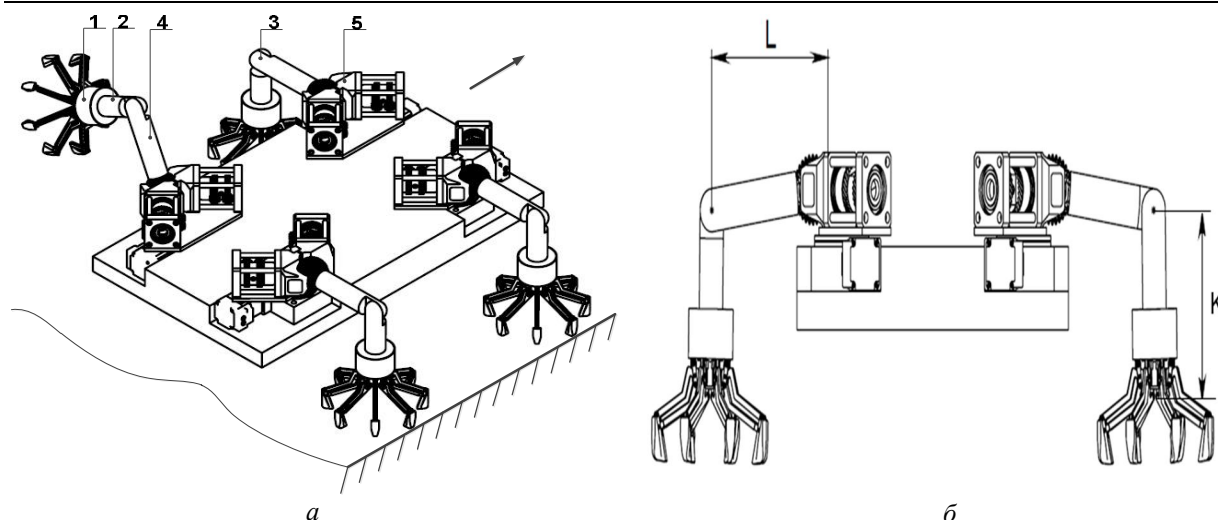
НПК з БМ: а – вид зверху; б – вид спереду
